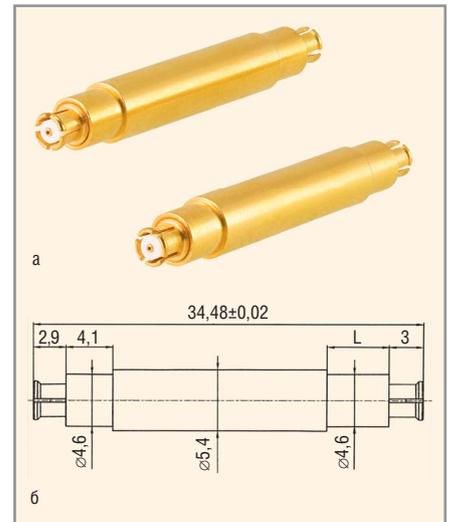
Соединитель SMP-РБНП-Х-1-329:
